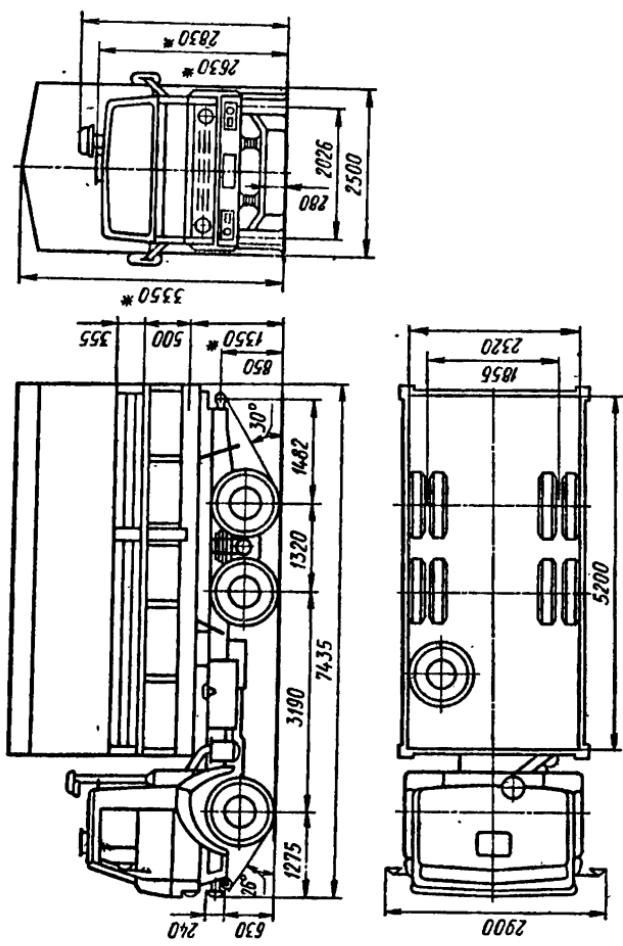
Габаритные размеры автомобиля КамАЗ-5320 (здесь и далее звездочкой отмечены размеры для снаряженного автомобиля)
